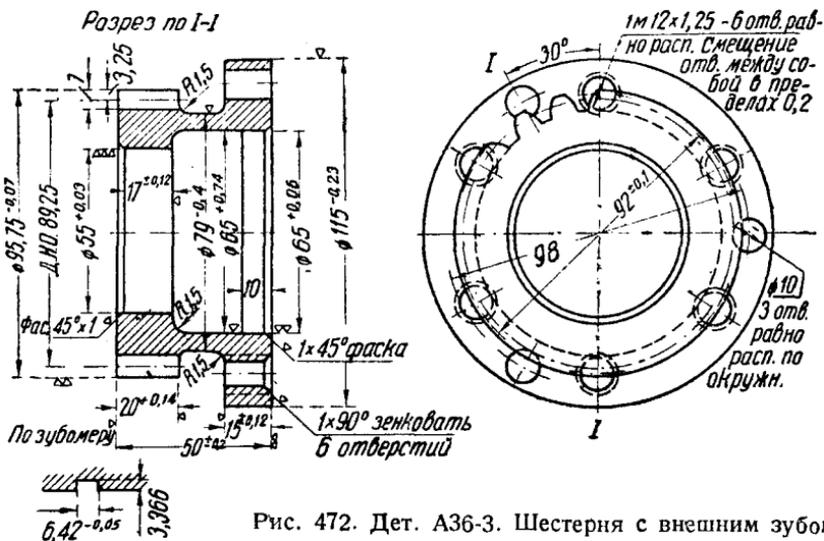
Дет. А36-3. Шестерня с внешним зубом
